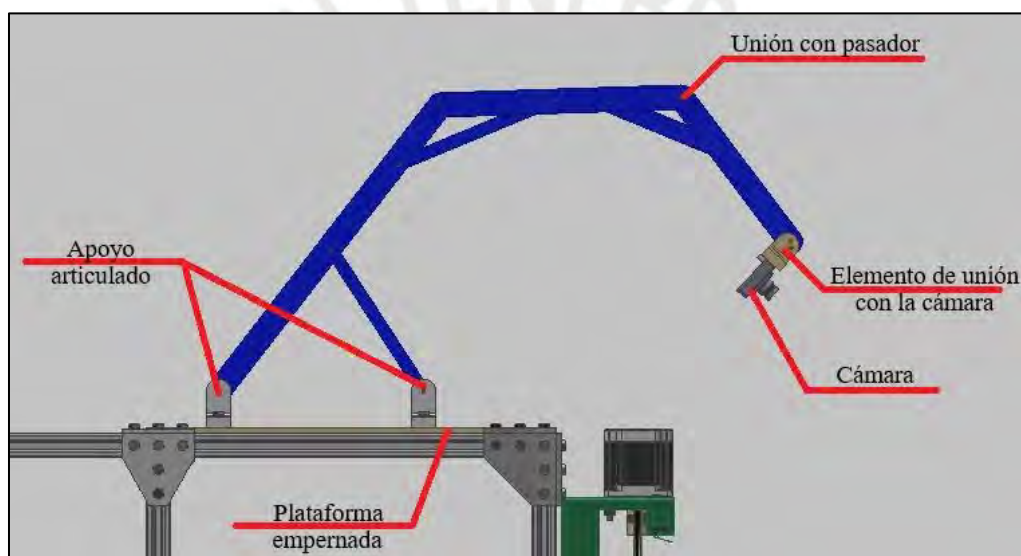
Detalle de la estructura de soporte de la cámara. Elaboración propia.
